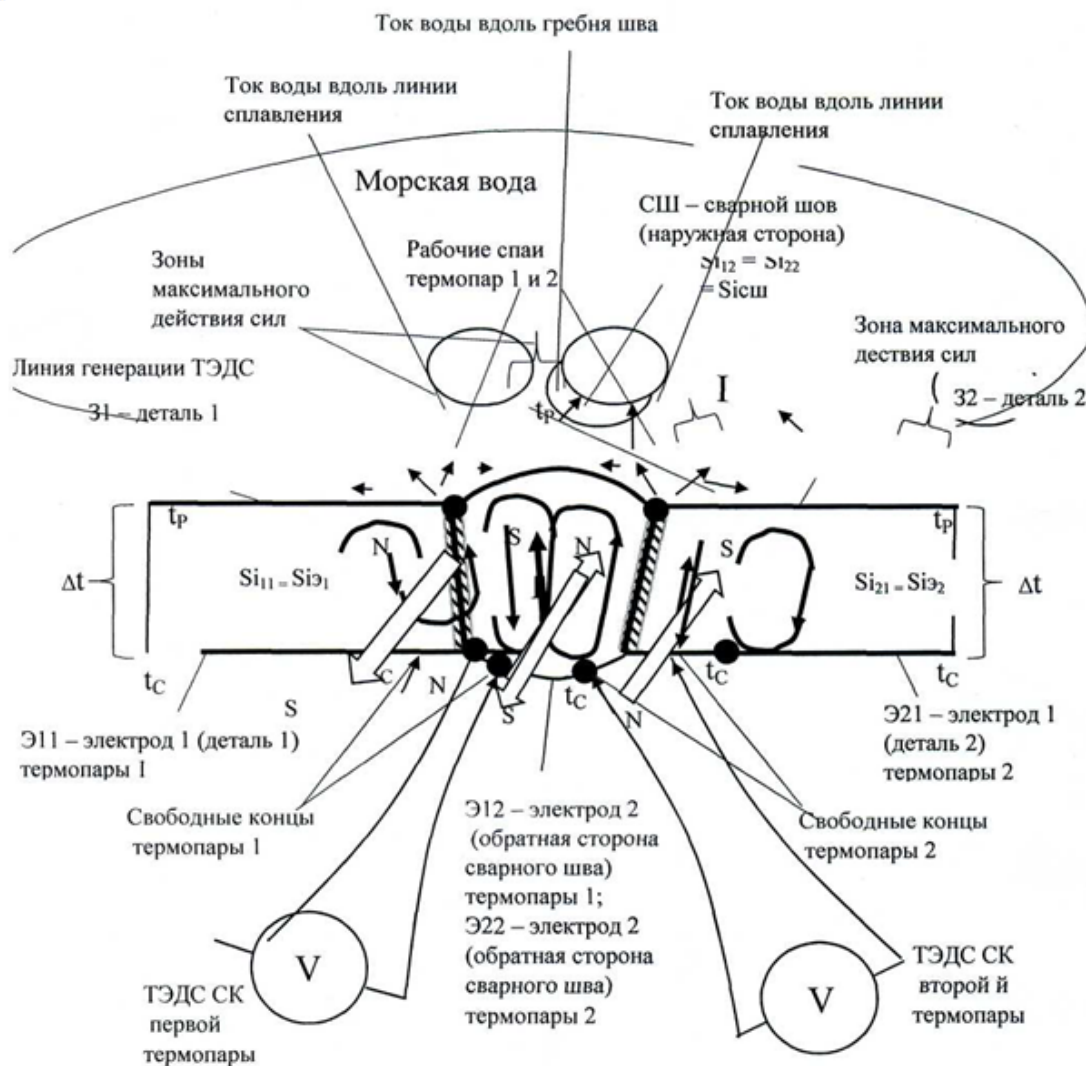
Схема формирования скрытой ТЭДС с нагревом сварного соединения по толщине обшивки судна
